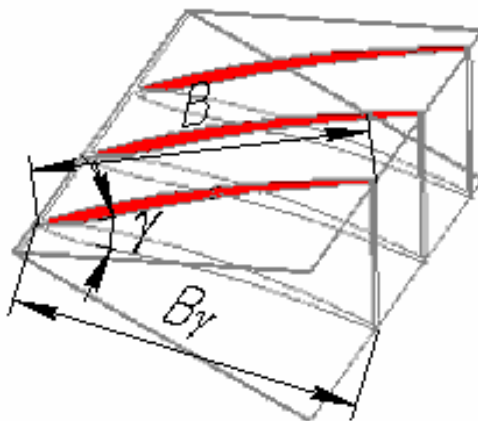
Искажение формы профиля при пересечении лопатки конической поверхностью
